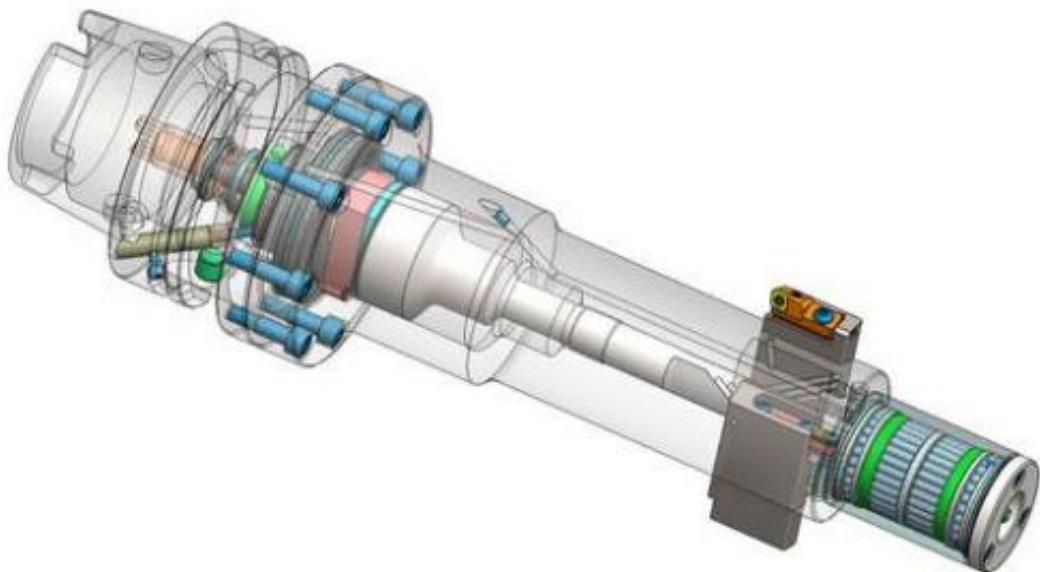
Модульна розточувальна головка ColonialTool [3]
